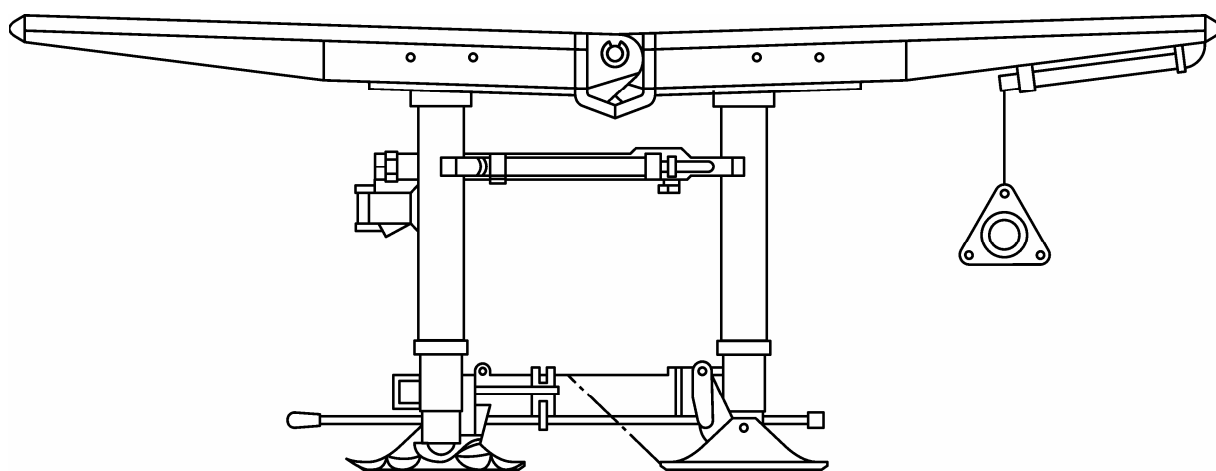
Схема секции механизированной крепи с подвеской закладочного трубопровода на завальной консоли перекрытия
